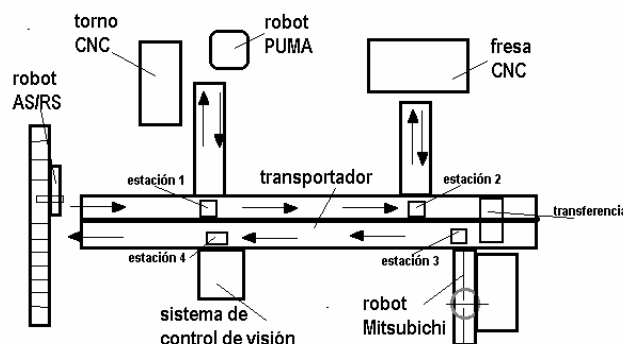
Croquis de la planta del Sistema Integrado de Manufactura empleado para la elaboración del conjunto ensamblado árbol – rueda dentada.
